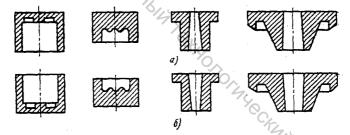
Отливки группы II (подгруппа A) для поршневого (a) и пуансонного (б) прессования
